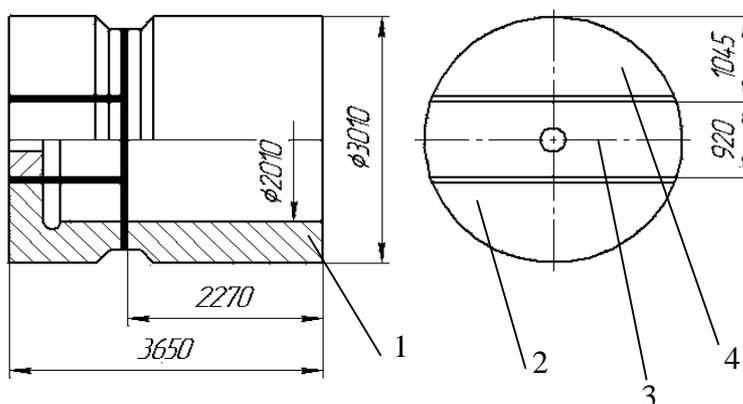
Общий вид цилиндра со сварным днищем:
